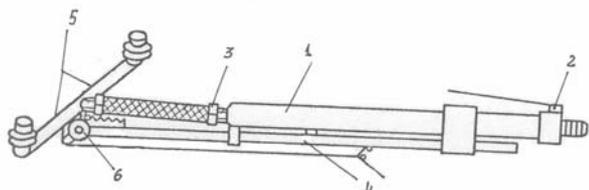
Штанга опрыскивателя животных: 1 – рабочая труба, 2 – запорный кран, 3 – соединительный шланг, 4 – несущая труба, 5 – рабочий орган, 6 – шарнирный механизм.
